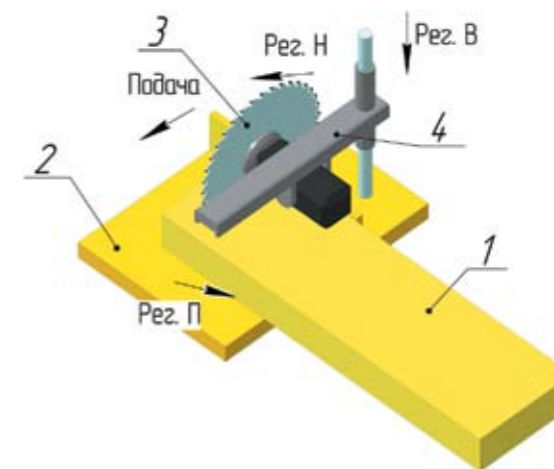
Торцовочный станок с горизонтальной подачей: 1 – заготовка; 2 – стол; 3 – пильный блок; 4 – консольная траверса с кареткой. Ограждение инструмента не показано
